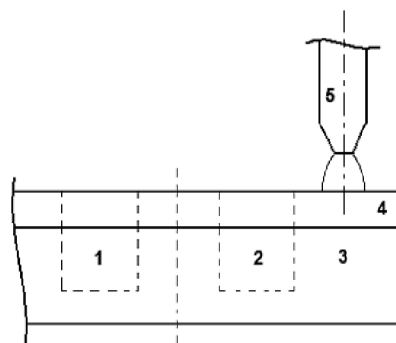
Схема переплавлення твердого сплаву: 1, 2 – ділянки для металографічних досліджень, 3 – основний метал, 4 – наплавлений шар
